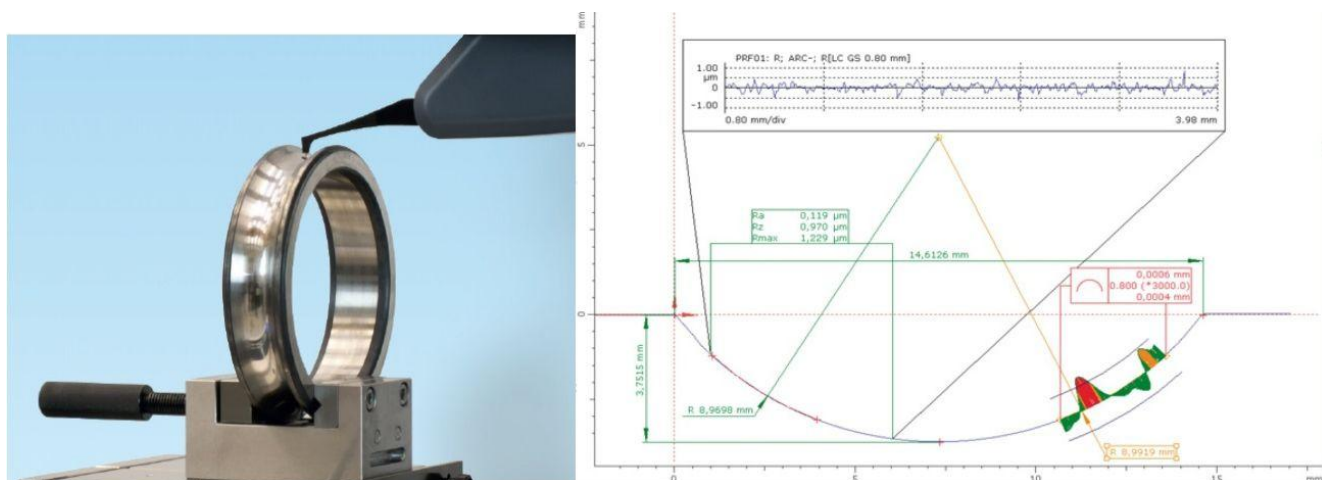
Пример оценки поверхности кольца подшипника.
